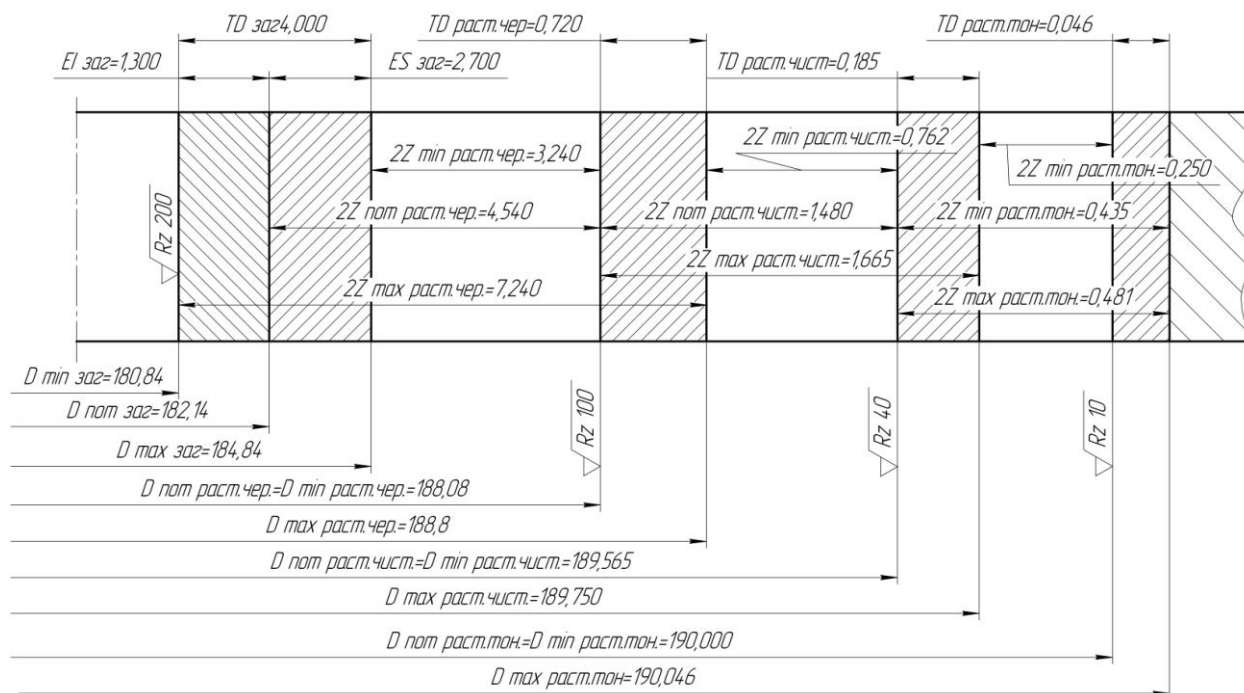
Схема расположения припусков и допусков для наружной цилиндрической поверхности $\text{Ø}190\text{H}7(0;+0,046)$
